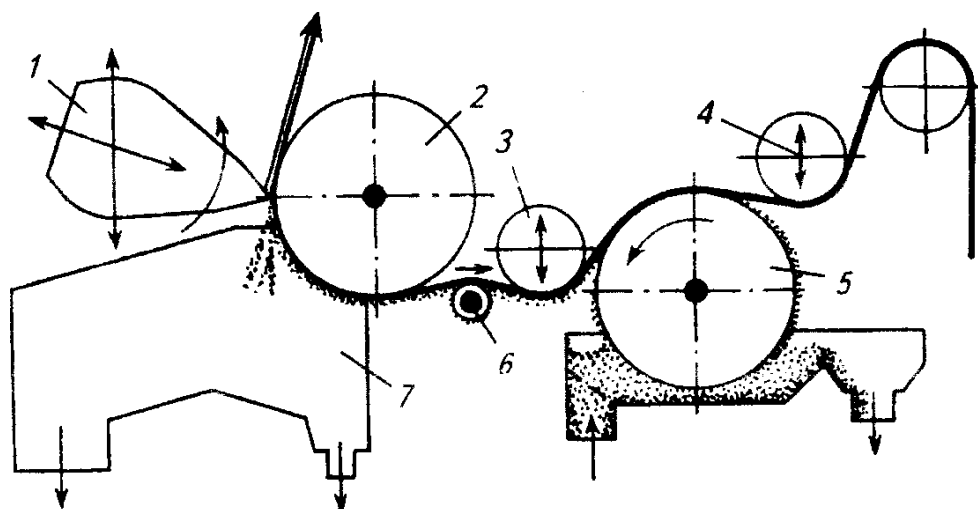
Схема нанесения покрытия с использованием воздушного шабера:
